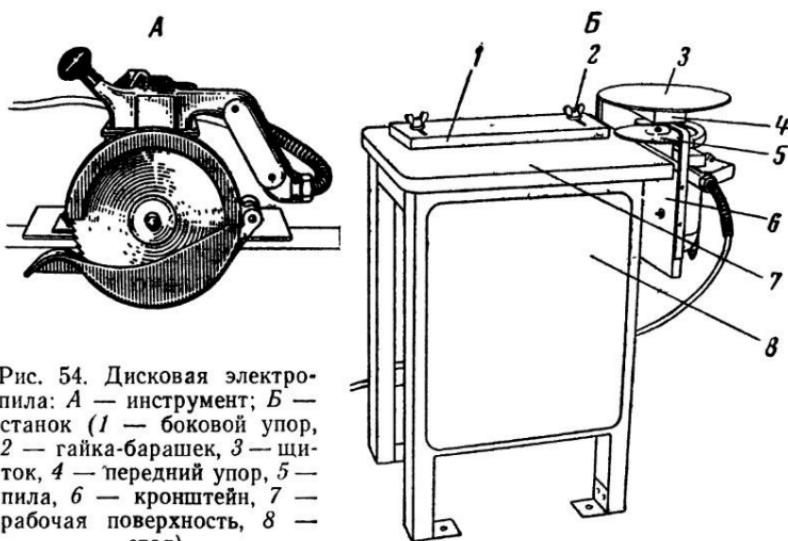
Дисковая электропила: А — инструмент; Б — станок (1 — боковой упор, 2 — гайка-барашек, 3 — щиток, 4 — передний упор, 5 — пила, 6 — кронштейн, 7 — рабочая поверхность, 8 — стол).
